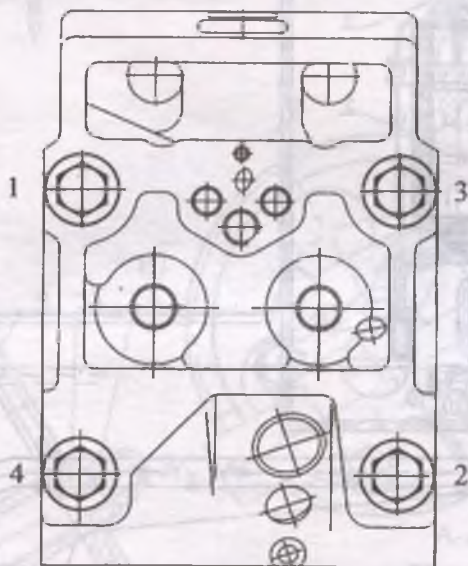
Последовательность затяжки болтов крепления головки цилиндра
